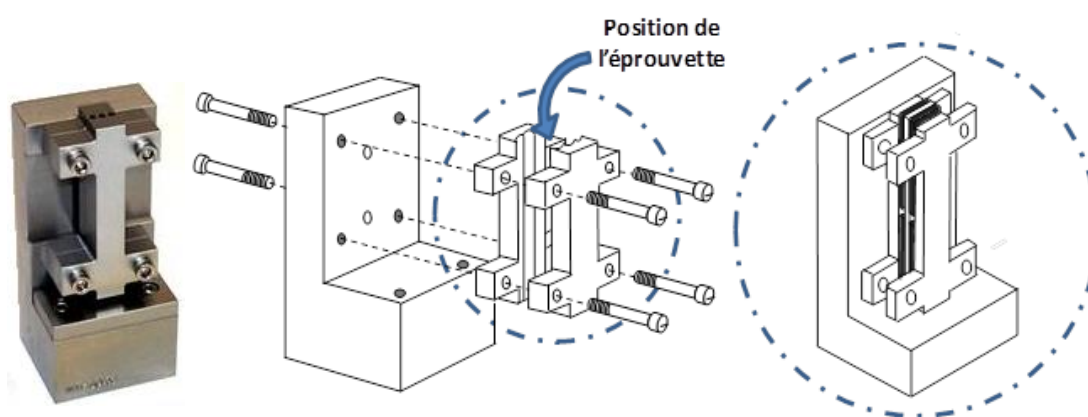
Montage type ASTM D 695 modifié par Boeing
